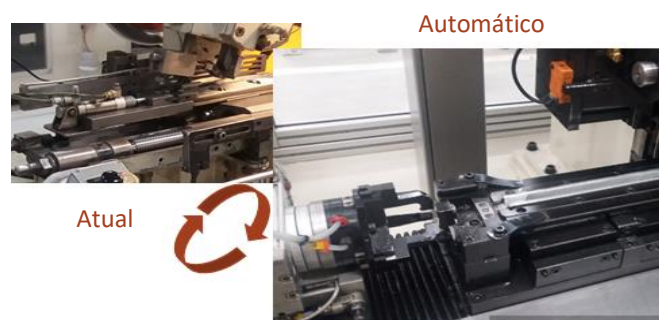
Máquina de picagem atual e máquina de picagem automática [SNA].
